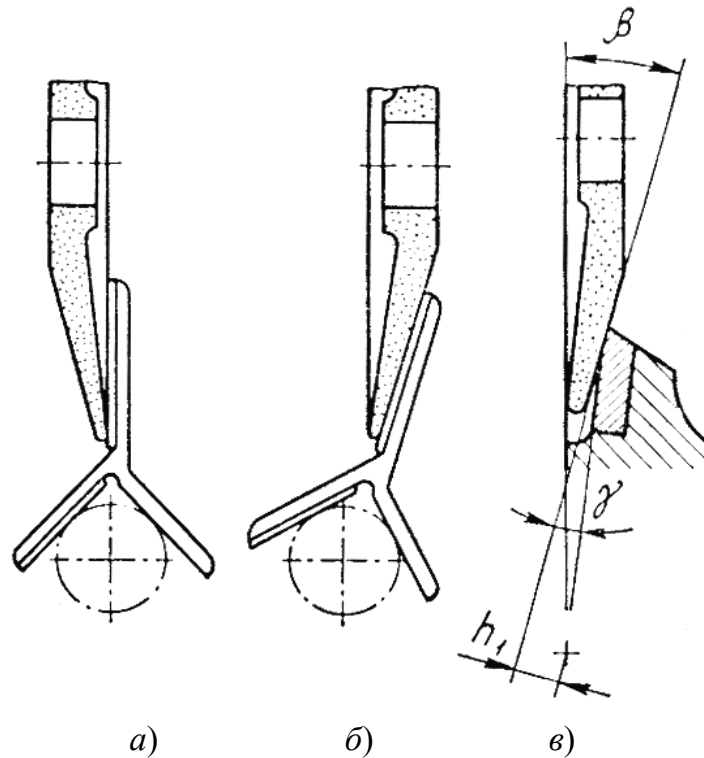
Установка абразивного инструмента при заточке передней поверхности инструмента:
